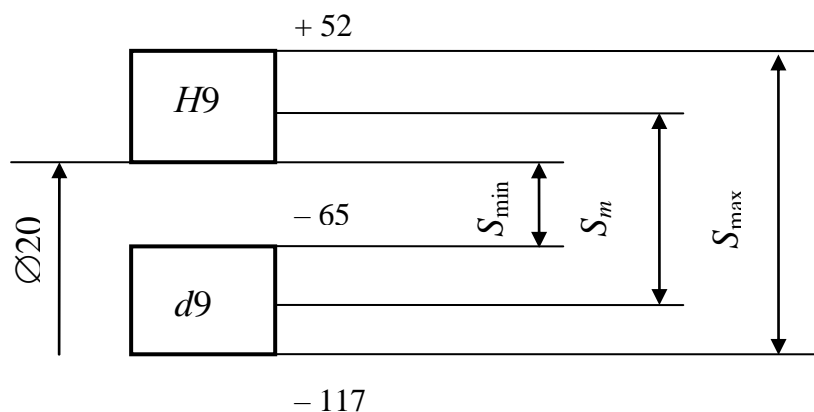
Схема расположения полей допусков посадки с зазором
